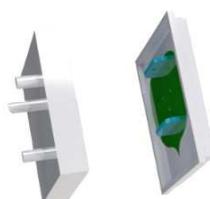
Partes diferenciadas del molde para el moldeo de una pieza.
